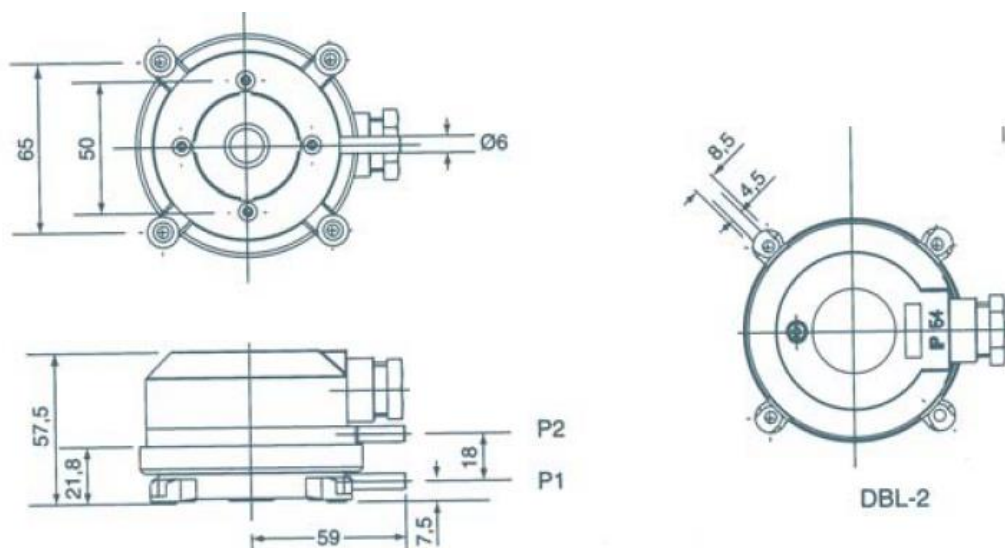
Габаритные размеры датчика давления DBL-205A
